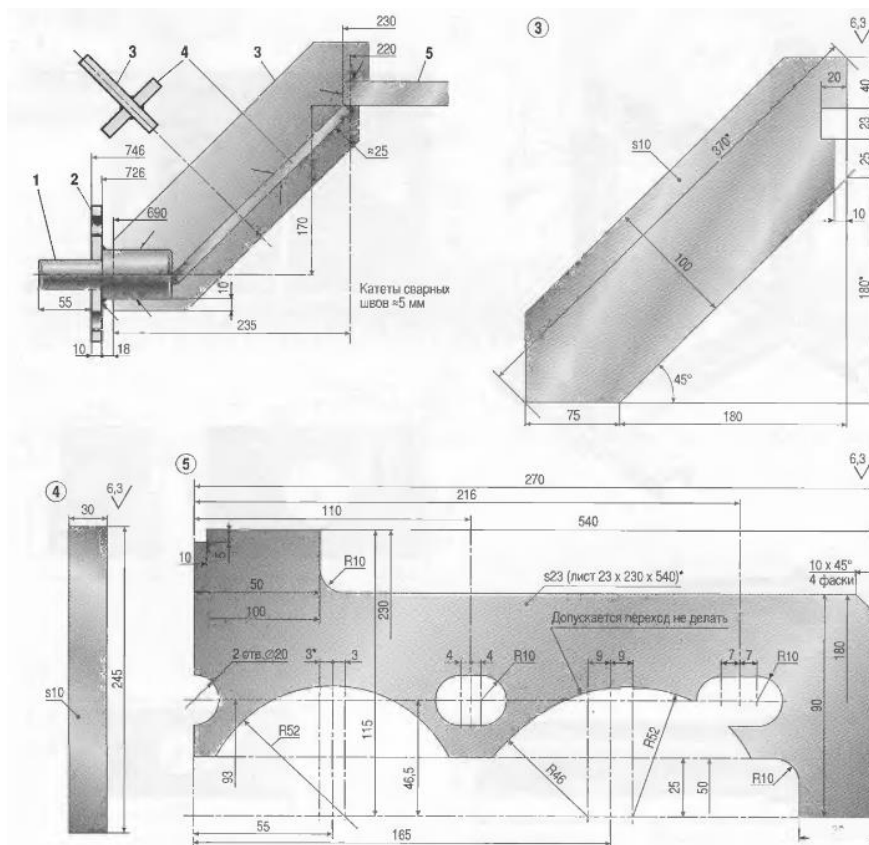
Вид механизма «Траверса блоков цилиндров»
